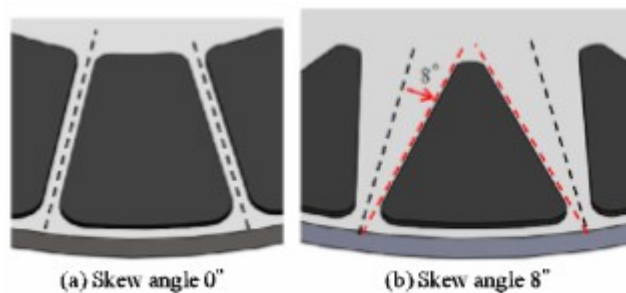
skewing del rotore – (a) 0° - (b) 8°
